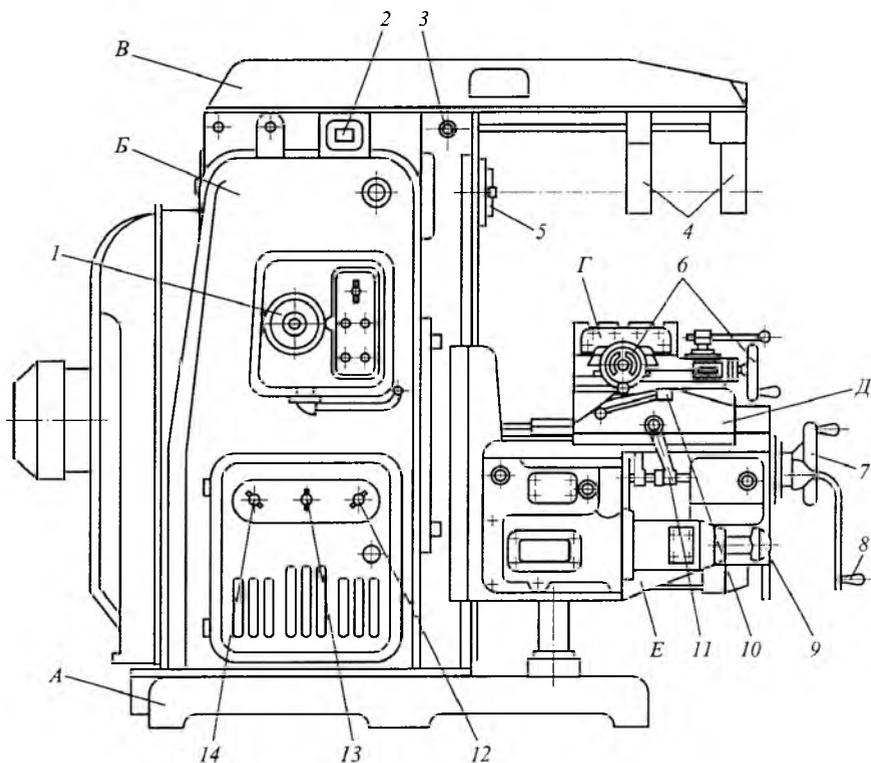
Консольный горизонтально-фрезерный станок:
